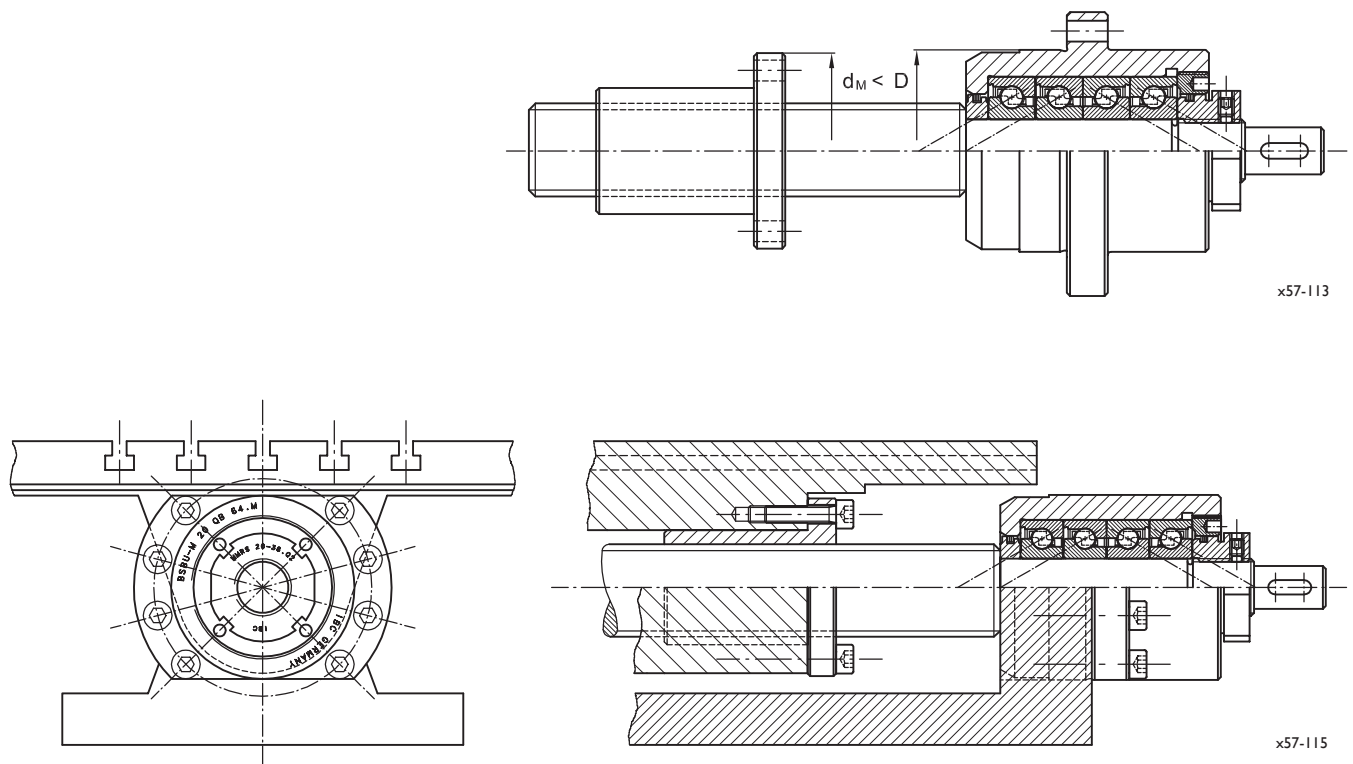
Vormontierte Baugruppe mit Kugelgewindetrieb und Präzisions-Flanschlagereinheit der Serie BSBU-M
